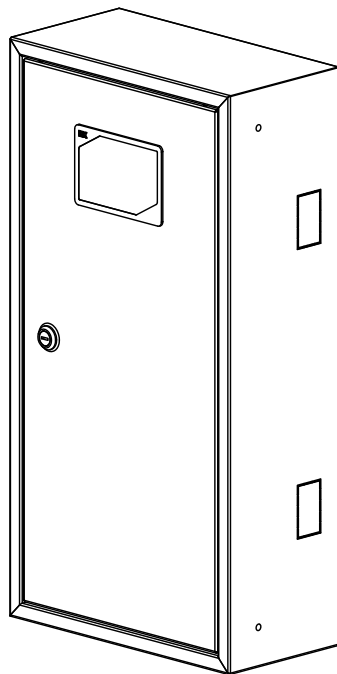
Общий вид корпуса ЯУР-3/12
